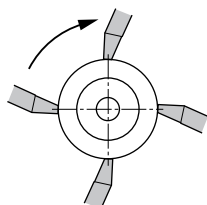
Kontrola axiálnej adjustácie pomocou posuvného meradla – priebežná kontrola
